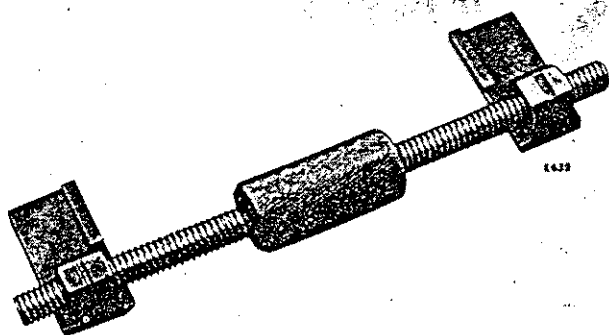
Spreizwerkzeug zum Einbau der Lenkungs Zahnstange
